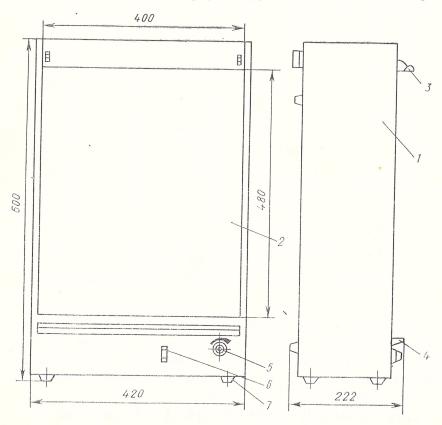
Негатоскоп общего назначения H-48 1 — корпус, 2 — экран; 3 — кронштейн; 4 — лоток; 5 — ручка регулировки яркости; 6 — выключатель; 7 — пожка.
